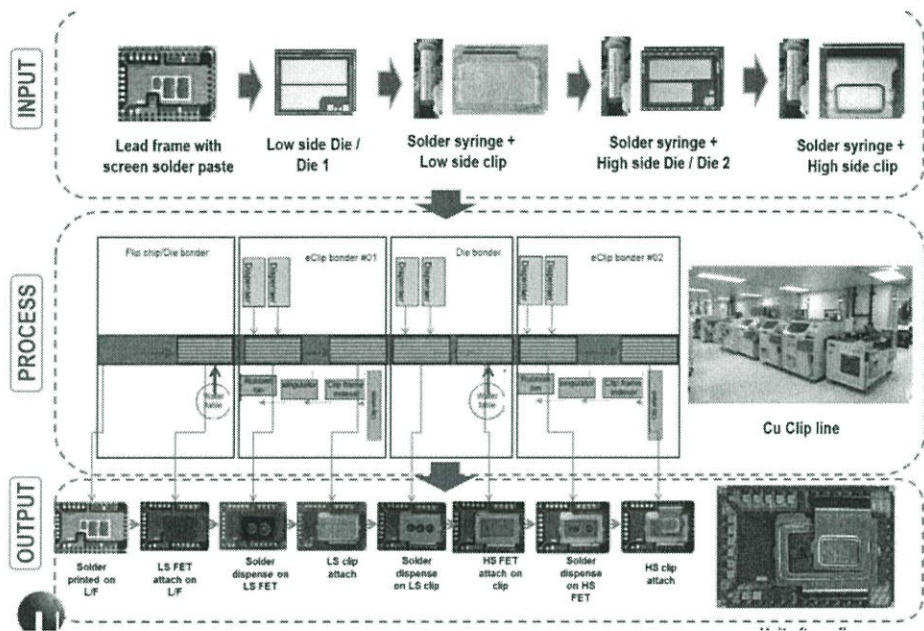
แสดงขั้นตอนการ Screen print Solder
